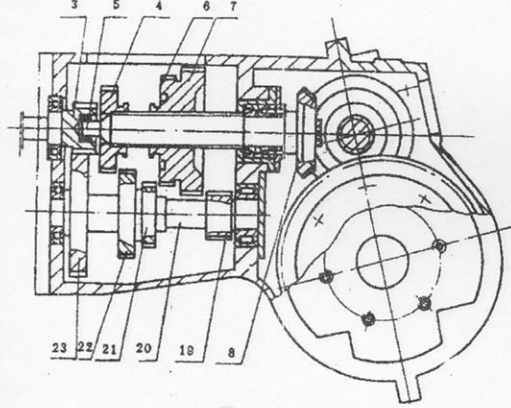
所示为换向机构，位于变速箱中部，在传动轴后端固定有小伞齿轮 8 与两个大伞齿轮啮合。两个大伞齿轮在换向轴 3 上作相反方向的空转，当滑动换向齿轮 16 与任一个大伞齿轮内齿啮合时，使 16 得到不同方向旋转而起到换向作用，齿轮 16 与差速器的大齿轮啮合。
